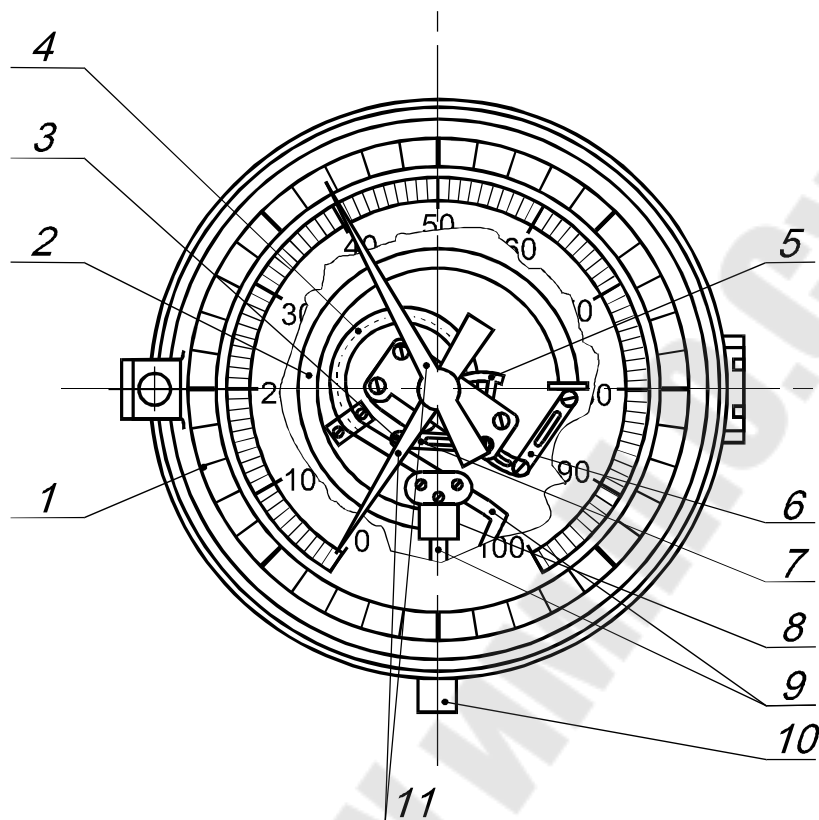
Манометрический механизм совмещенного указателя с основной и верньерной шкалой: 1 – корпус; 2 – манометрическая пружина верньерного механизма; 3 – основной трибо-секторный механизм; 4 – манометрическая пружина основного механизма; 5 – верньерный трибо-секторный механизм; 6 – тяги верньерного механизма; 7 – тяги основного механизма; 8 – держатель; 9 – трубопровод; 10 – тройник; 11 – стрелки.
